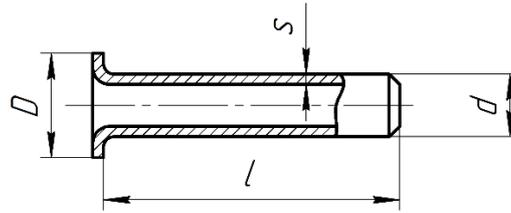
Основные геометрические параметры трубчатой заклепки
